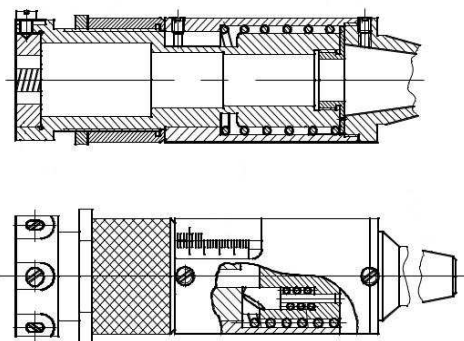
Патрон для кріплення плашки на токарному верстаті (схема)
